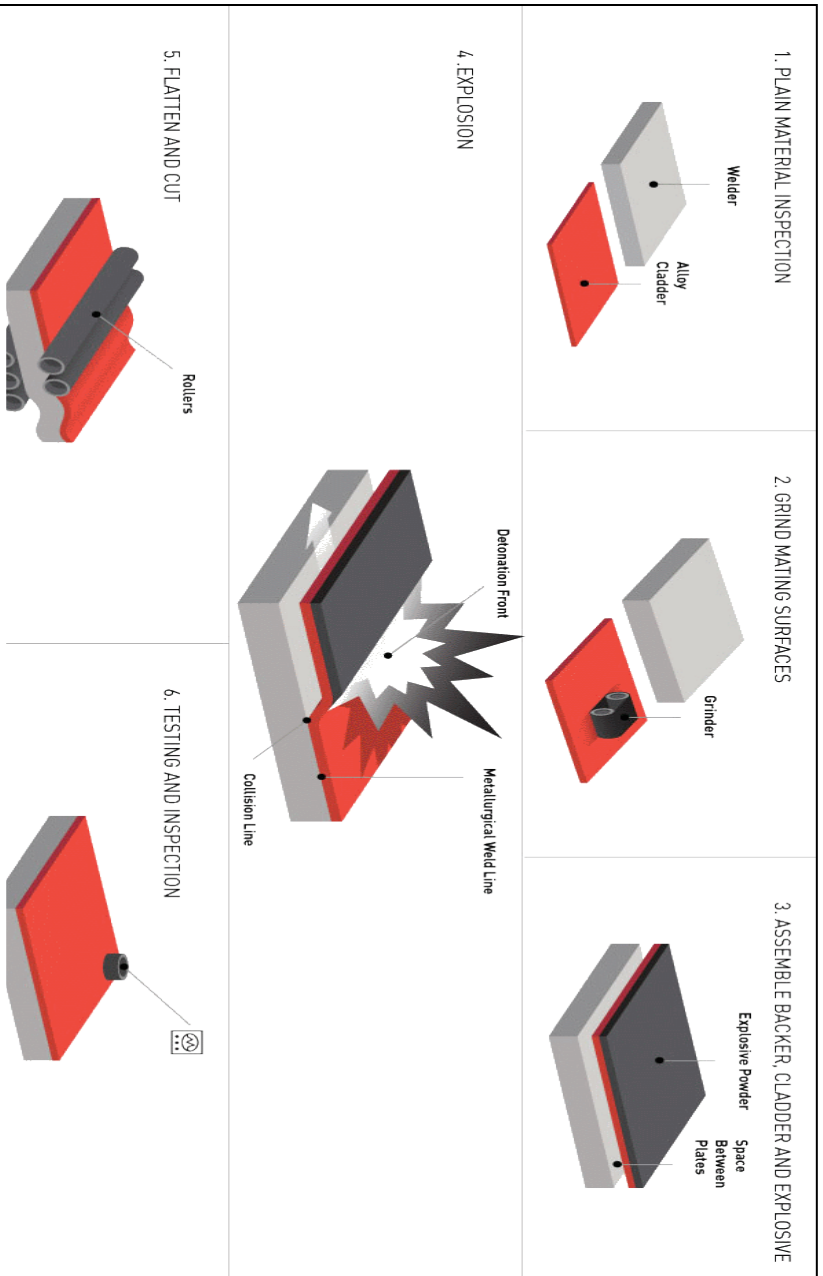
Etapes d'une opération de soudage explosive
